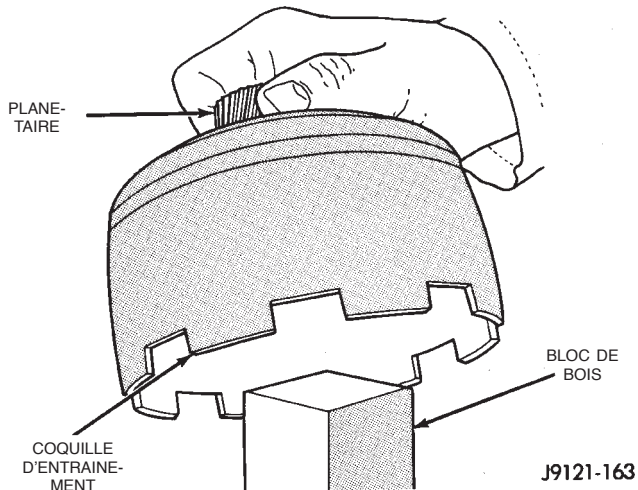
Pose de plateau de butée arrière de coquille d'entraînement
